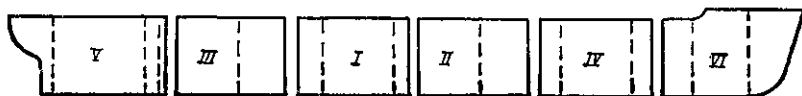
Схема разбивки и сборки корпуса при блочном способе строительства: I — закладной блок, II—VI — очередность установки блоков на стапеле
